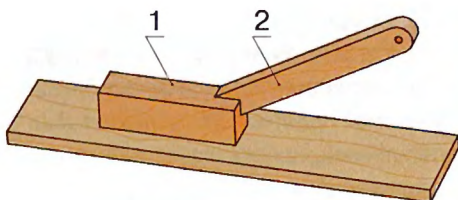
Использование толкателя: 1 — заготовка; 2 — толкатель.
